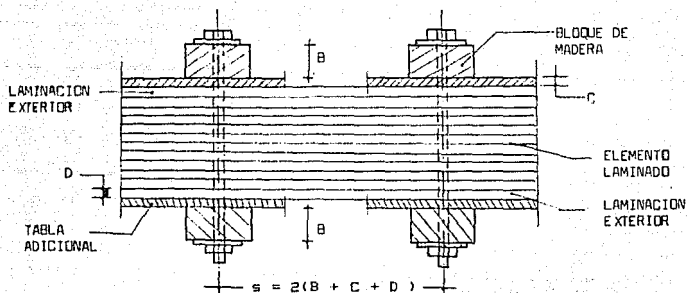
Sistema de prensado de vigas de madera laminada.
